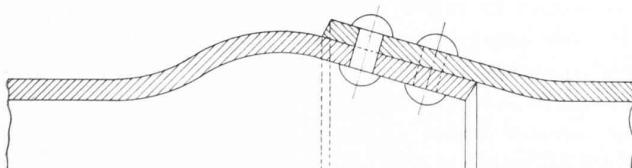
Joint tronc-conique à double ligne de rivets en zig-zag.
